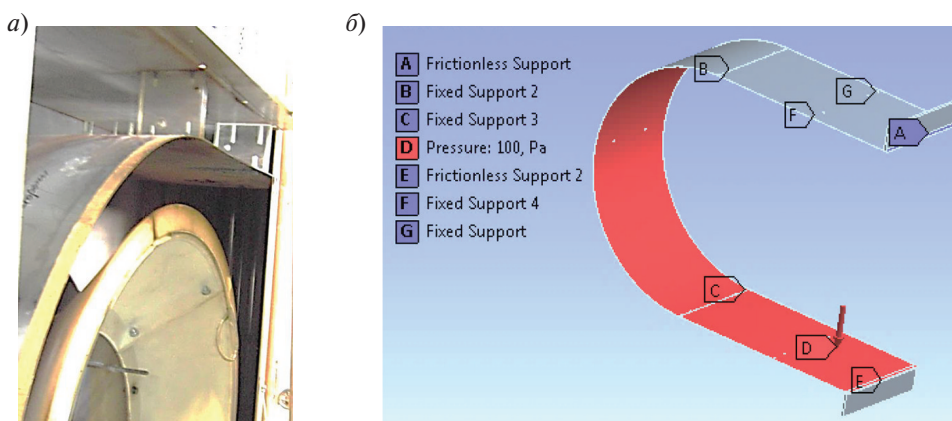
Общий вид (*a*) и расчетная схема закрепления (*б*) тонкостенной детали, образующей боковую поверхность патрубка
